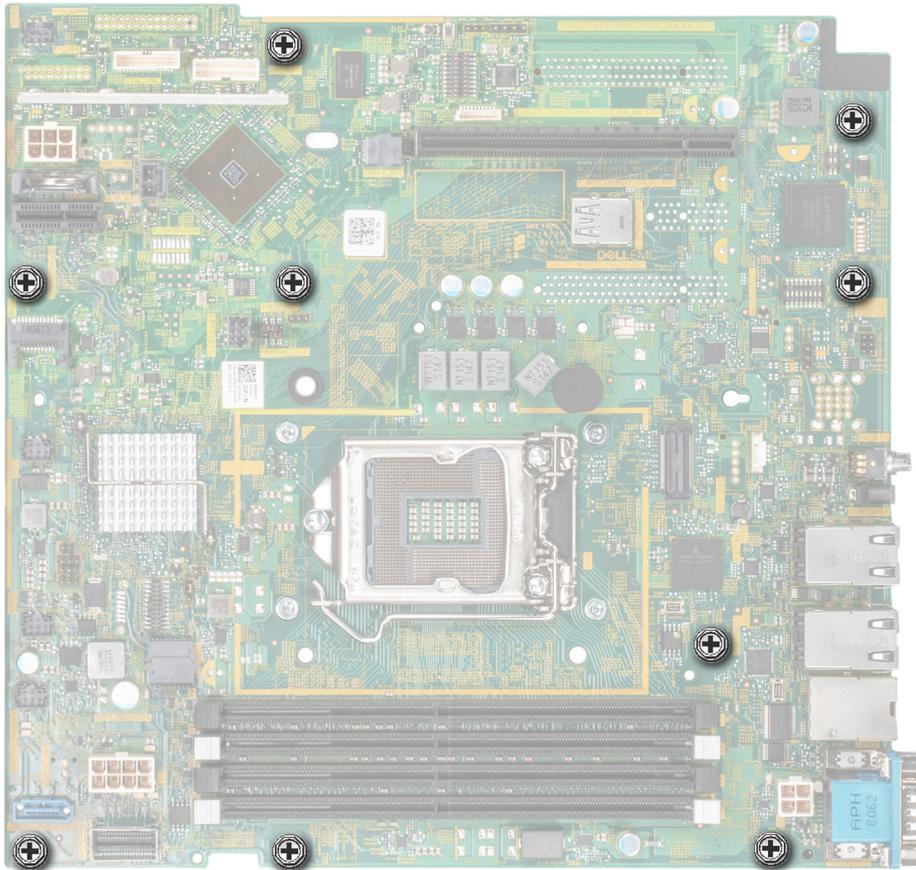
Schrauben, mit denen die Systemplatine befestigt ist
